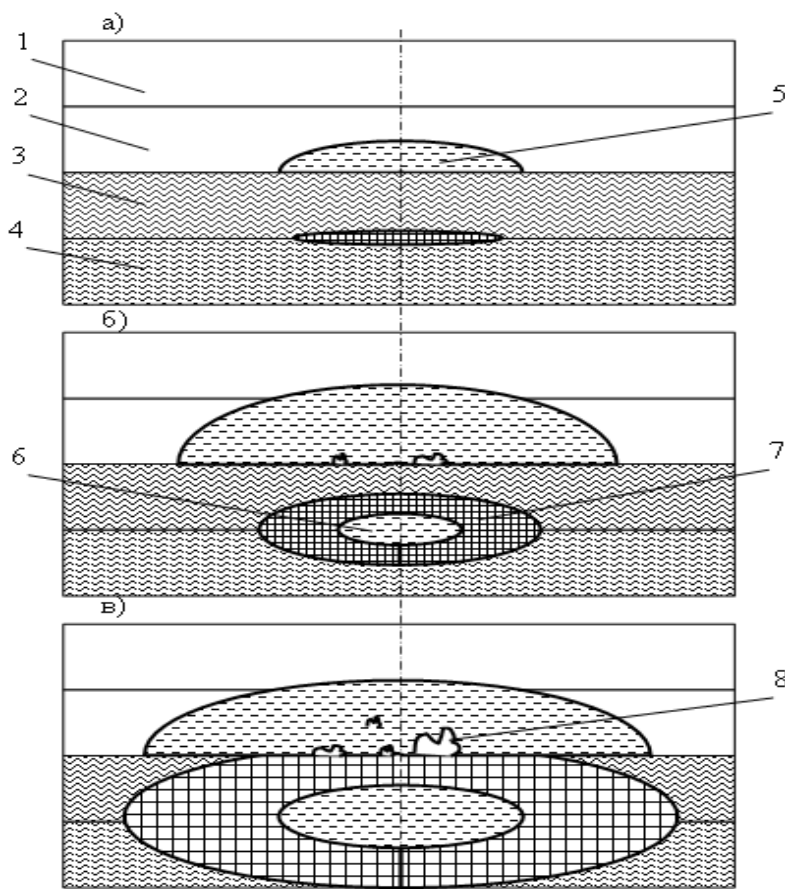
Механизм формирования сварного шва соединения «алюминий-переходник-сталь»
